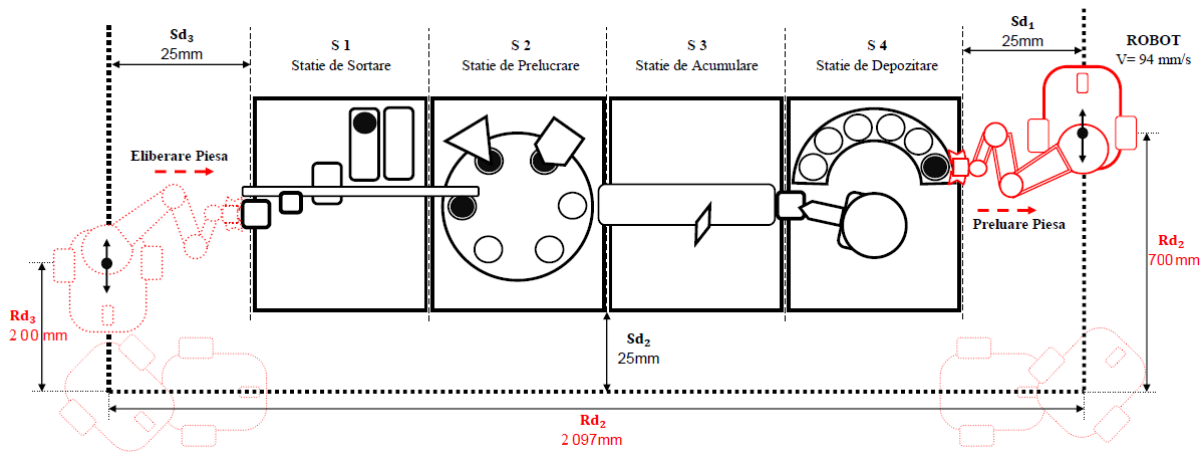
Linia de prelucrare FESTO MPS-300 deservita de robot mobil echipat cu manipulator
